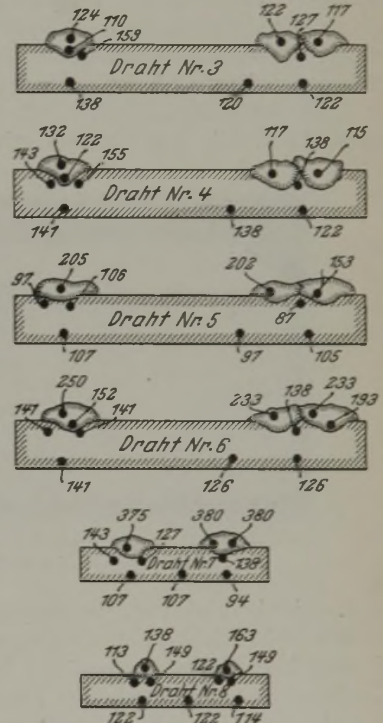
Raupenquerschnitte bei Auftragschweißungen mit Angabe ihrer Brinellhärte.
